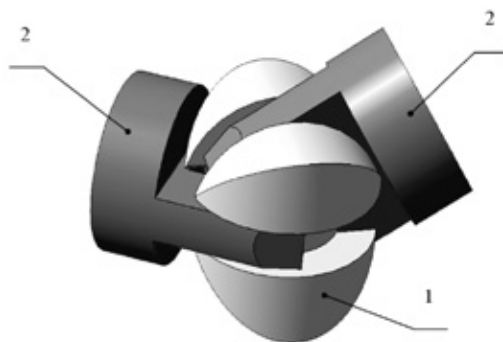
Конструкция карданного механизма [1]: 1 — муфта-звёздочка, 2 — вилка
